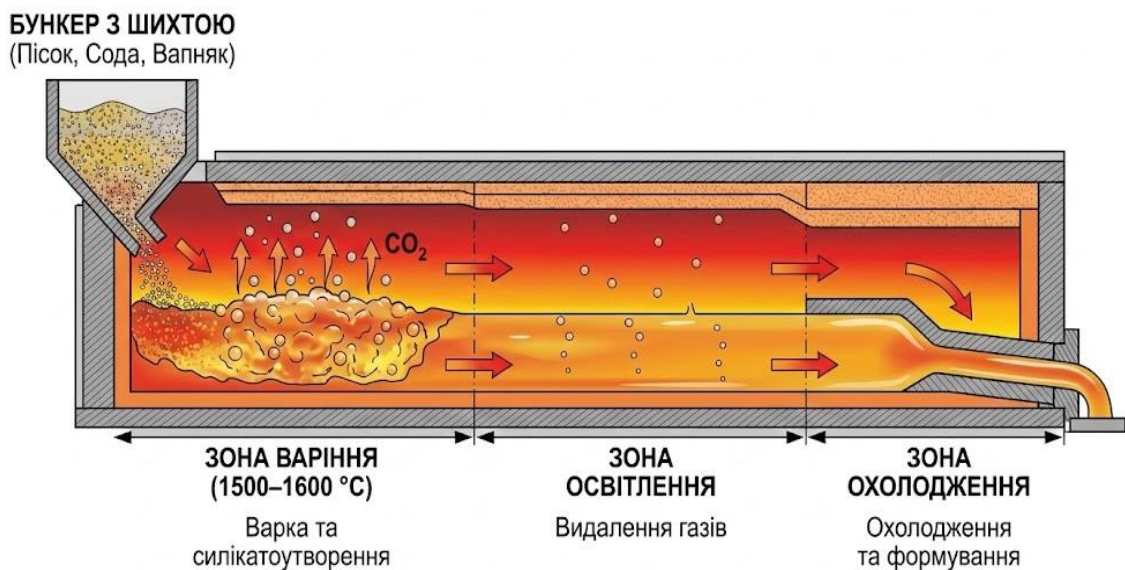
Принципова схема ванної печі для виготовлення скла
